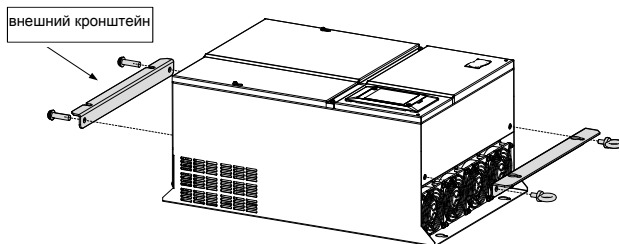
Сквозной монтаж ME320LN (металлический корпус)
